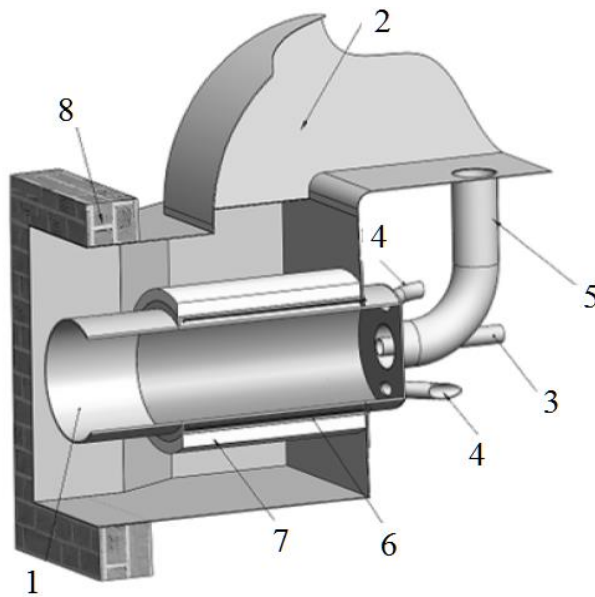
Эскиз универсального энергоэффективного горелочного устройства: 1 — реакционная труба; 2 — короб подвода вторичного воздуха; 3 — устройство подвода пыли высокой концентрации (ПВК); 4 — тангенциальный патрубок подачи первичного воздуха; 5 — патрубок осевой подачи первичного воздуха; 6 — система нагрева; 7 — тепловая изоляция; 8 — амбразура котла.
